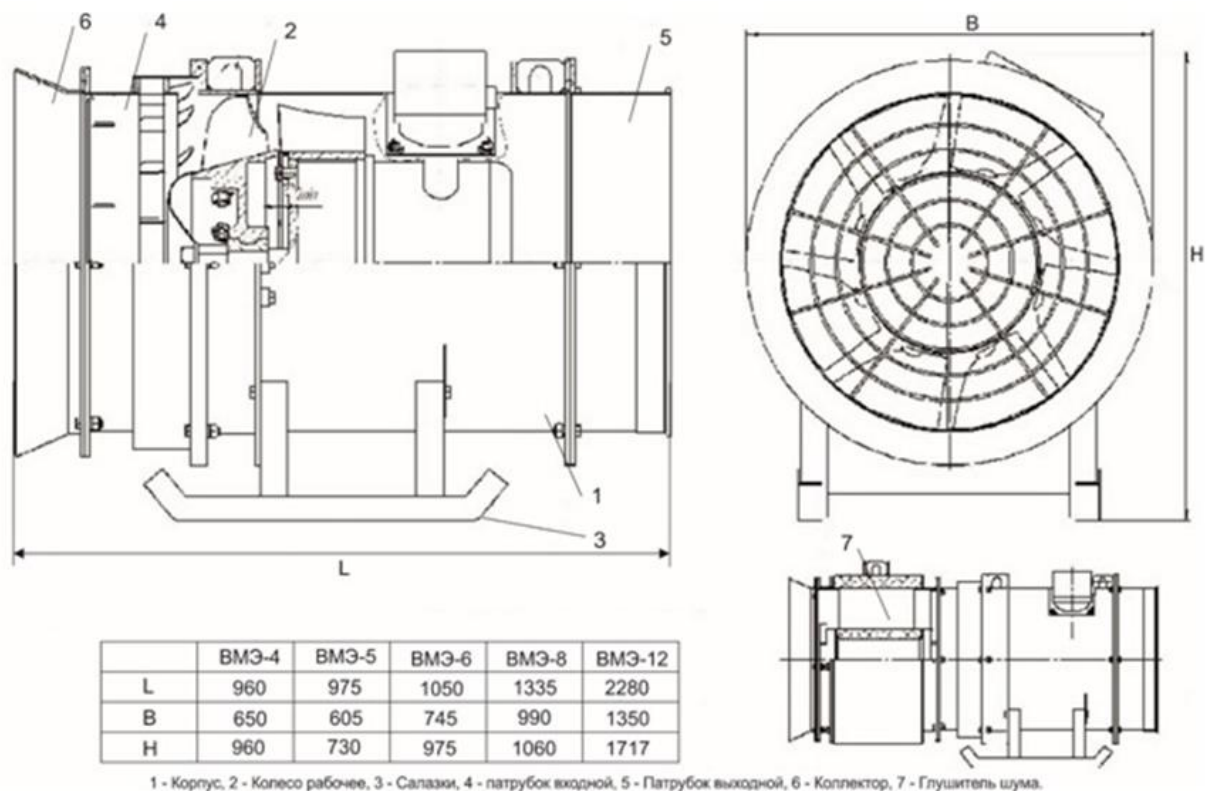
Чертеж общего вида вентилятора с размерами.
